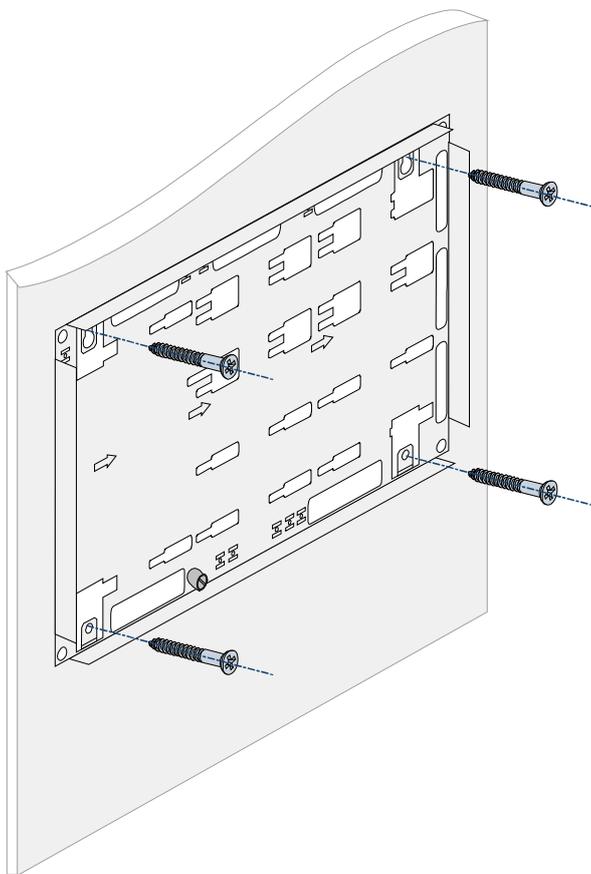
Befestigung auf der Montagefläche (Beispiel mit Rückwand für den waagerechten Ausbau)
